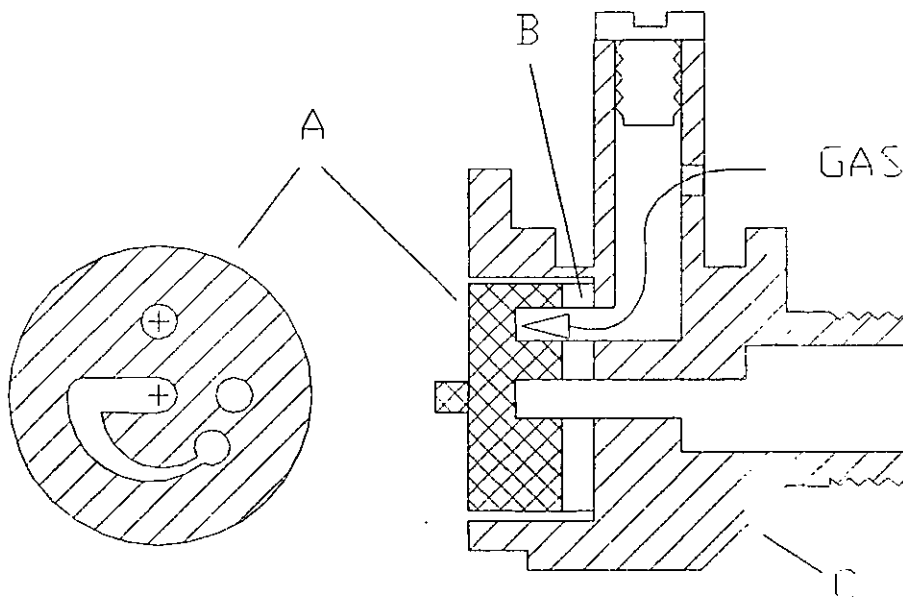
Corte transversal de válvula de disco ranurado (cerrada)
